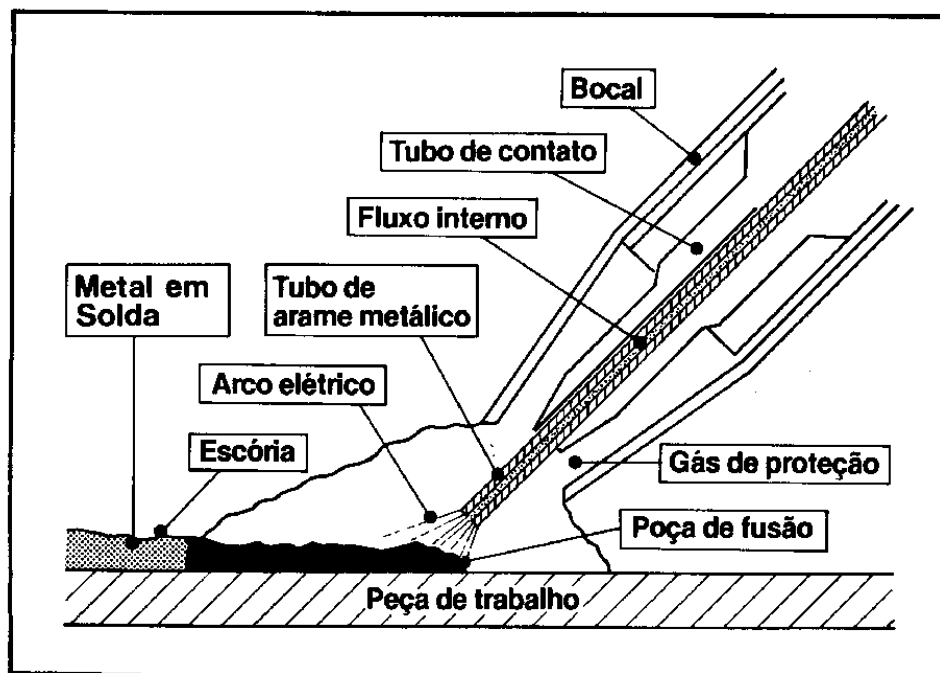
Tocha de soldagem do processo de soldagem com arames tubulares
